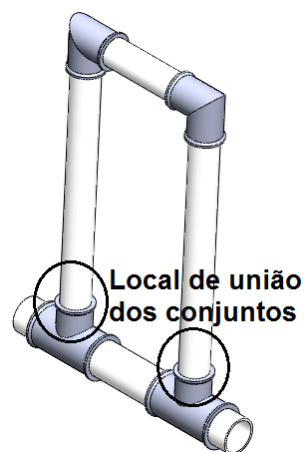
Montagem dos módulos – Módulo 3 – Passo 5
